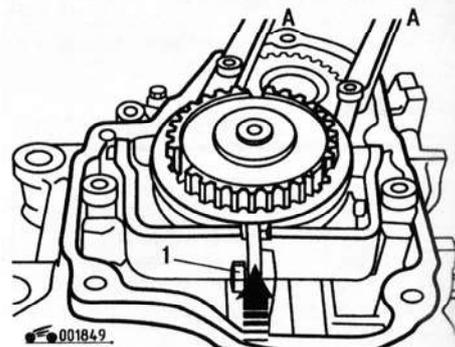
Регулировка положения вилки включения V передачи: А – щупы толщиной 1,2 мм; 1 – болт крепления рычага (стрелкой указано направление отжатия вилки при регулировке)
